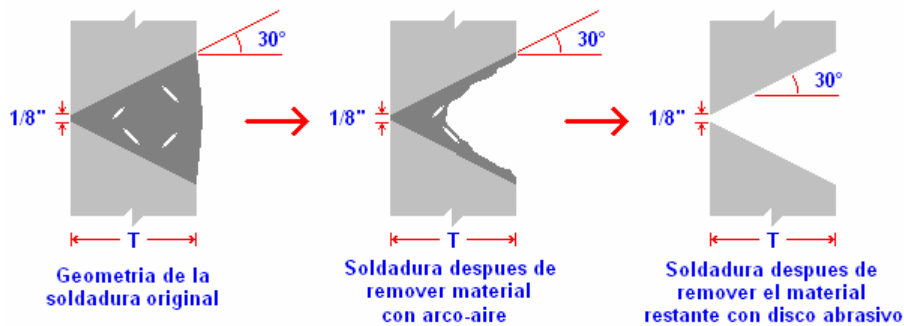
Remoción de la soldadura con defectos.
